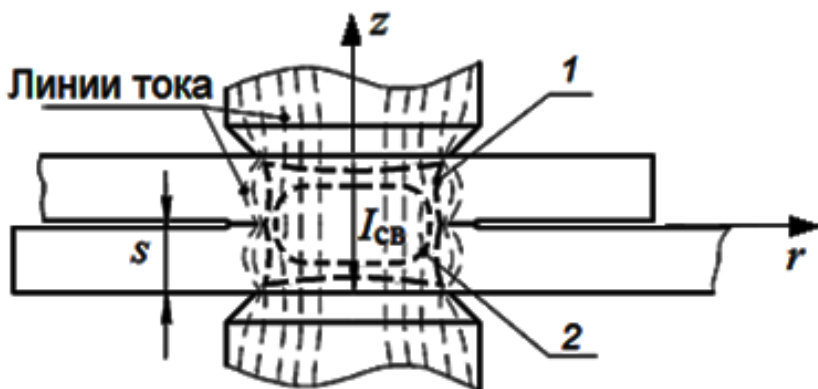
Форма ядра при сварке на жестких (1) и мягких (2) режимах
